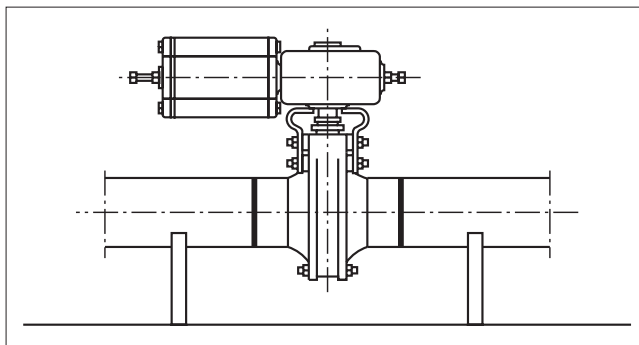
Support de la vanne d'extrémité de soudage
